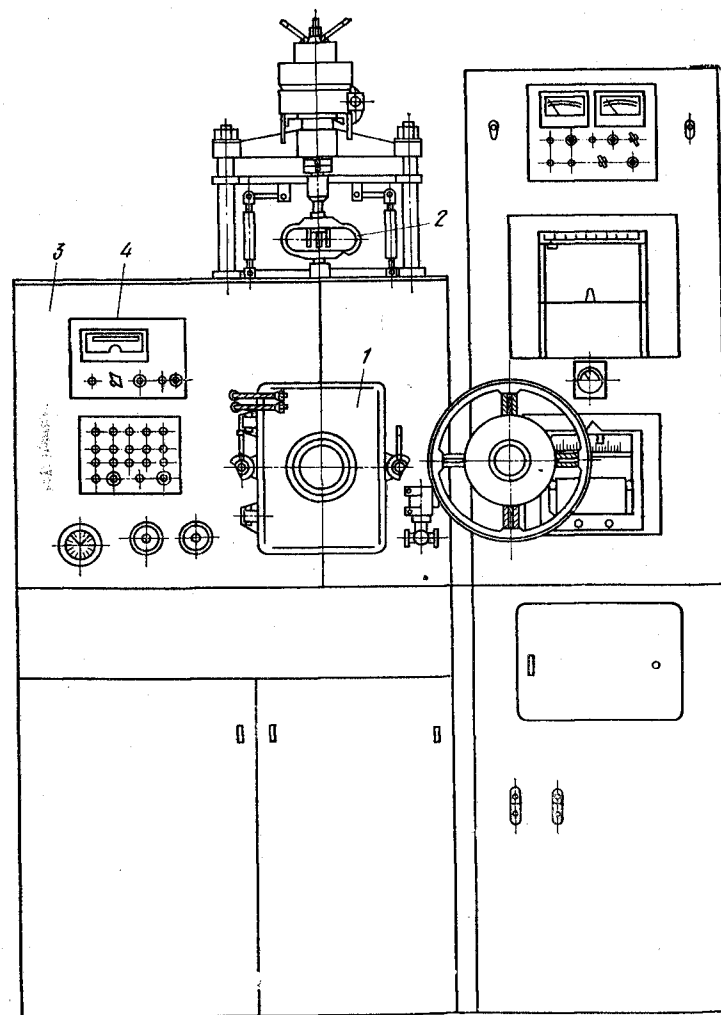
Установка диффузионной сварки в вакууме типа СДВУ-50
